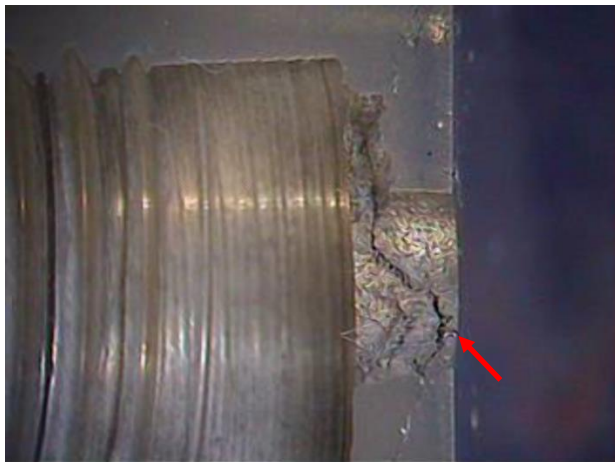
Ejemplo de las grietas localizadas en el fondo del barreno roscado de la pieza fundida (7x). Fuente: elaboración propia.
